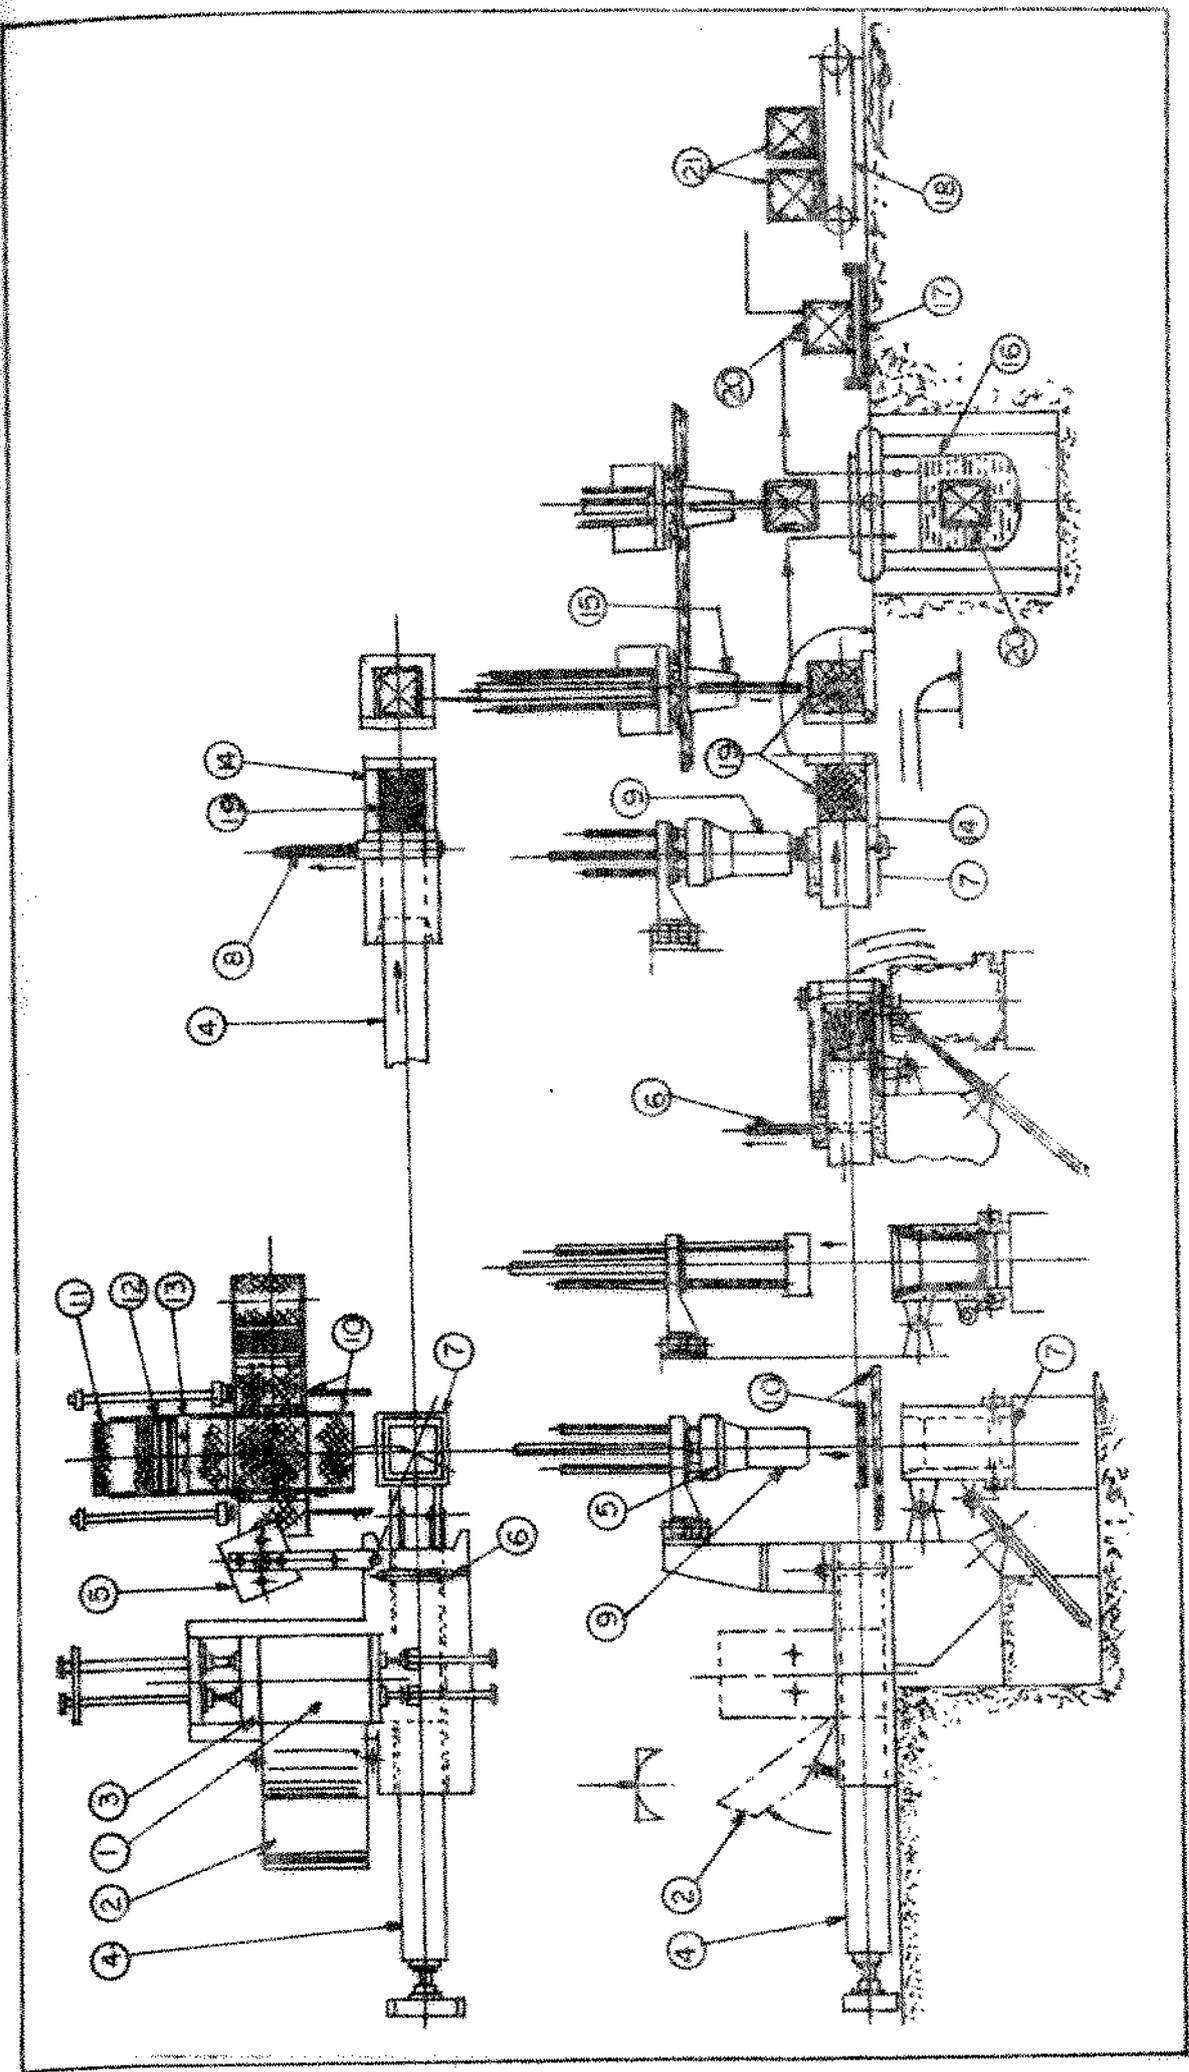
c - Usina de Compressão do Lixo de Montagem Horizontal.
